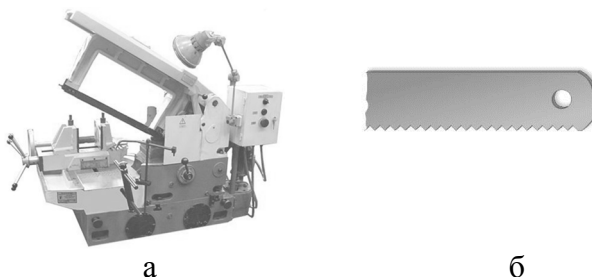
Зовнішній вигляд обладнання - привідної ножівки (а) та інструмента – ножівкового полотна (б)
